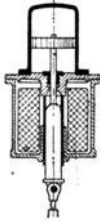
Hubmagnet mit geradliniger Bewegung.
